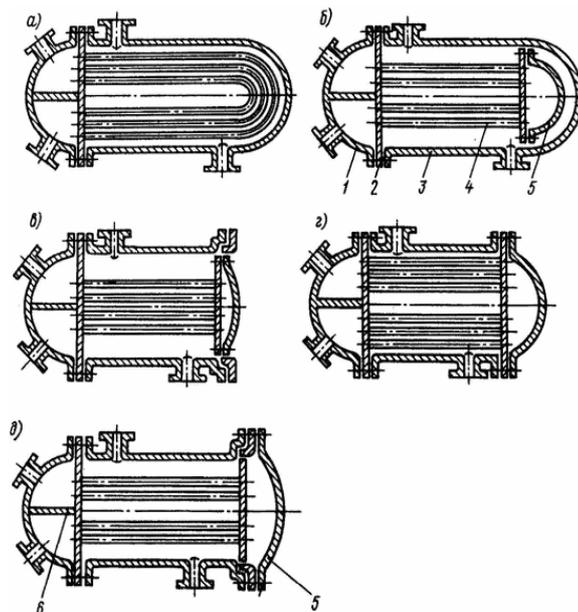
Схемы кожухотрубных теплообменников: а — с U-об-разными трубками; б — с плавающей трубной доской; в — с подвижной трубной доской и крышкой; г — с двумя неподвижно закрепленными трубными досками; д — с подвижной трубной доской и неподвижной крышкой
